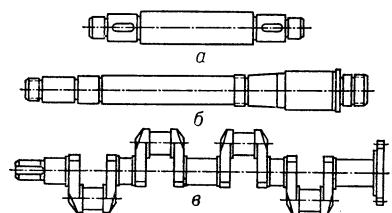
Валы и оси: а — вал ступенчатый; б — шпиндель металлорежущего станка; в — вал коленчатый.
